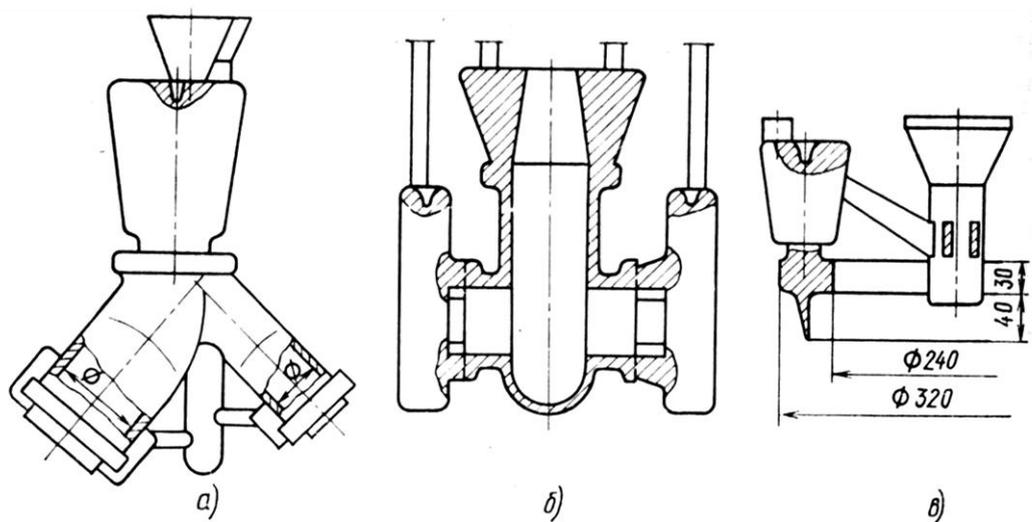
Литниково-питающая система типа VIII (система местных прибылей): а – тройник; б – корпус вентиля; в – кольцевой корпус.
